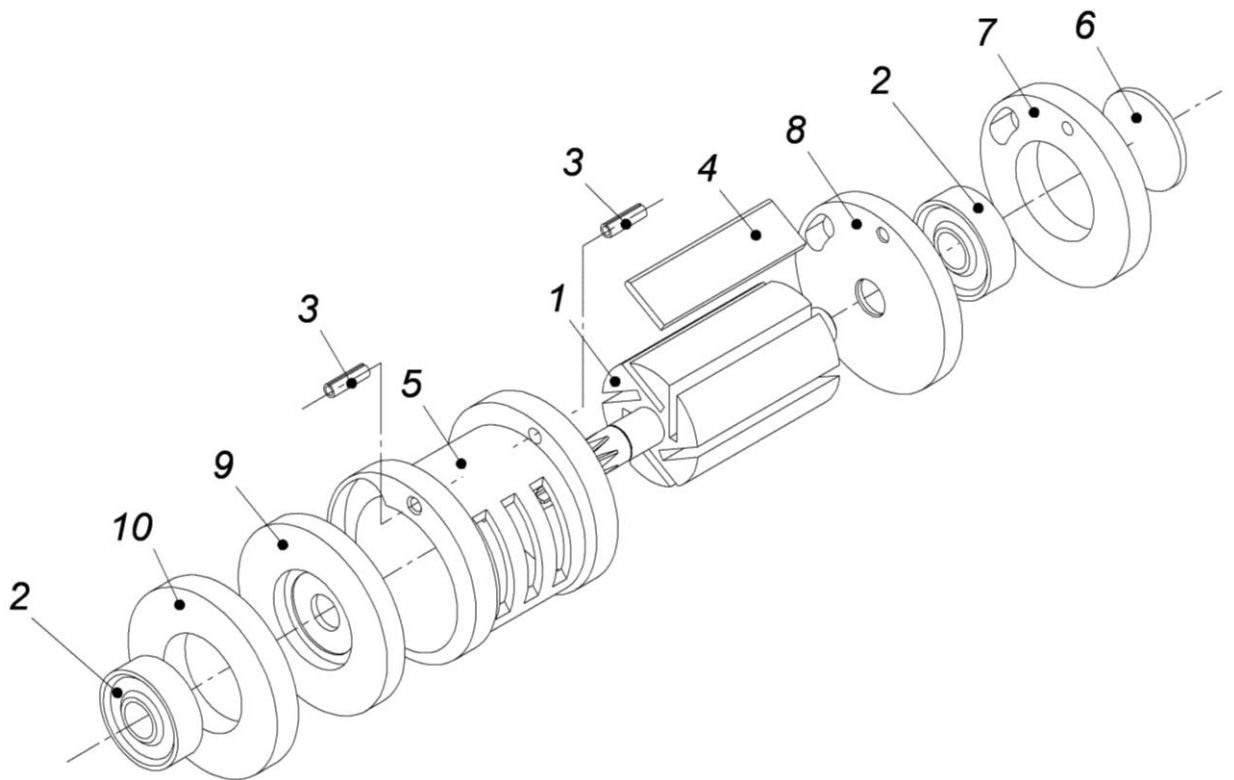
Мотор нереверсивный в сборе (пневмодвигатель)
